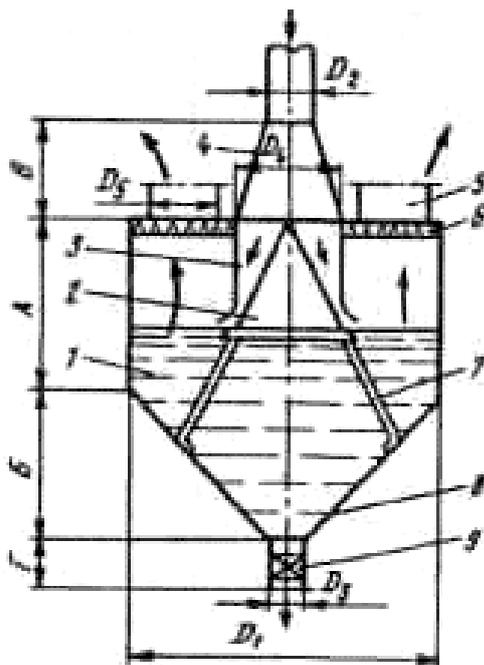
Мокрый пылеуловитель РИСИ: 1 — цилиндрическая камера; 2 — конус-рассекатель; 3 — отражатель; 4 — диффузор; 5 — патрубок для отвода воздуха; 6 — каплеуловитель; 7 — лапки для крепления; 8 — бункер конической формы; 9 — патрубок для стока шлама.
